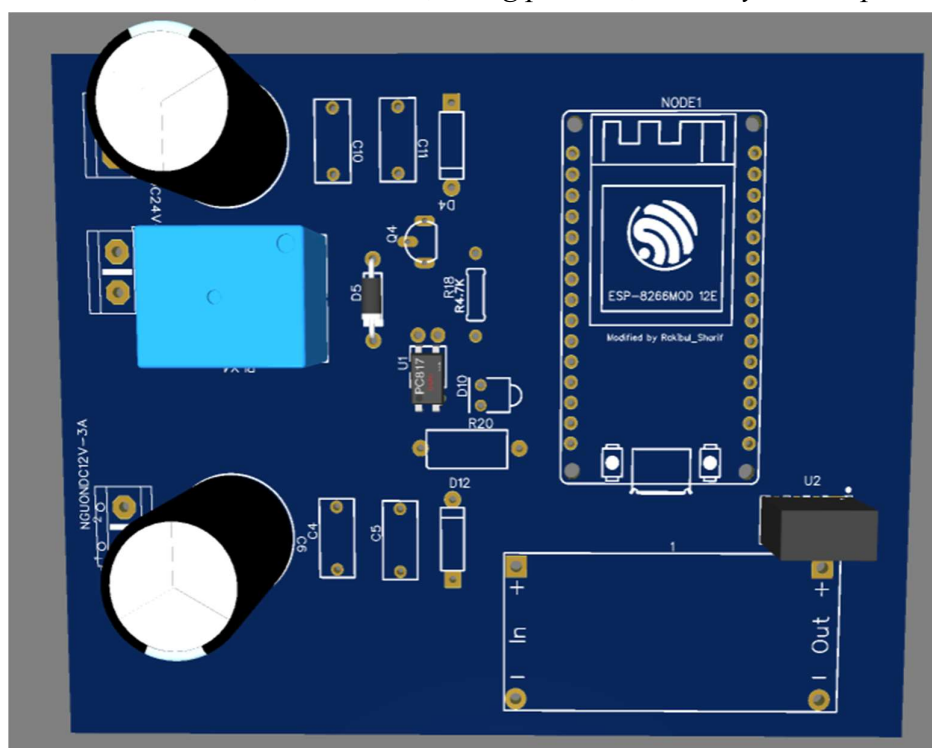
Sơ đồ mạch in PCB hệ thống cấp nhận tự động
